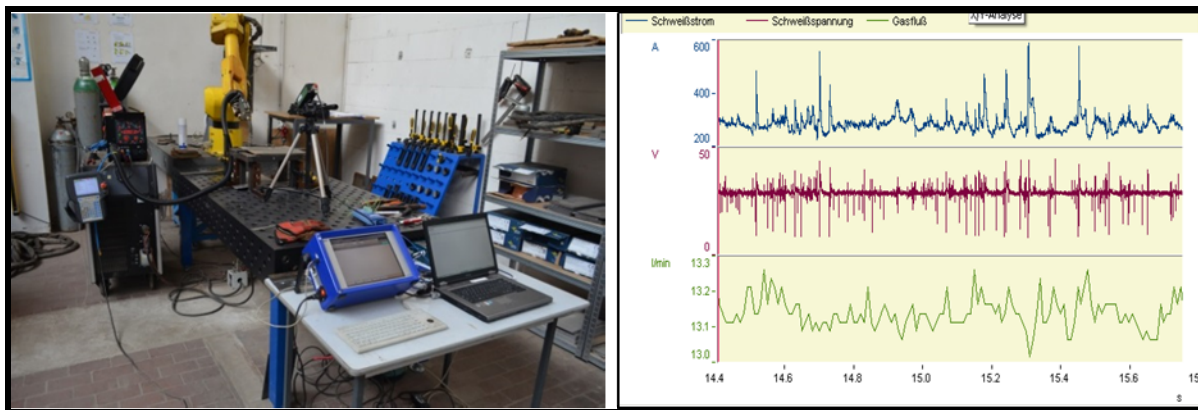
Versuchsstand MSG-Schweißen mit Roboter (links) und Aufzeichnung eines Schweißprozesses mittels HKS-System (rechts)
